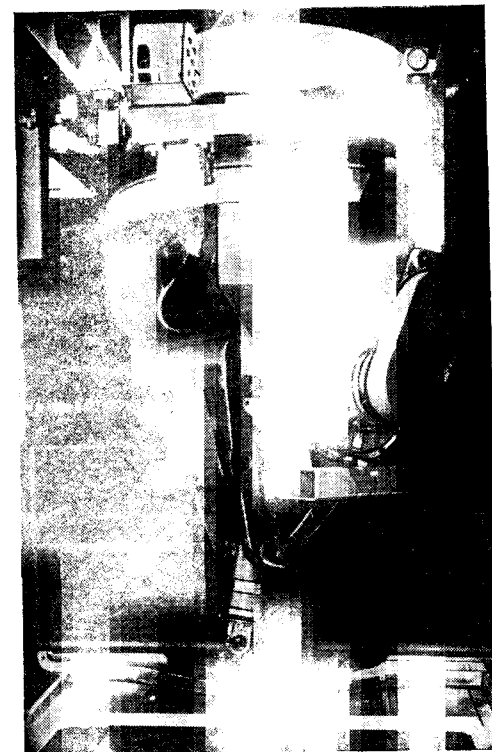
Сварочный ПР фирмы КУКА
